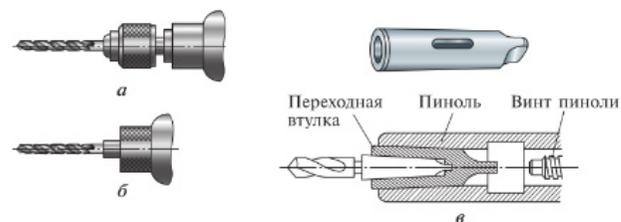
Установка сверла в пиноли задней бабки токарного станка: а — с помощью сверлильного патрона; б — с коническим хвостовиком в пиноли; в — с коническим хвостовиком в переходной втулке
